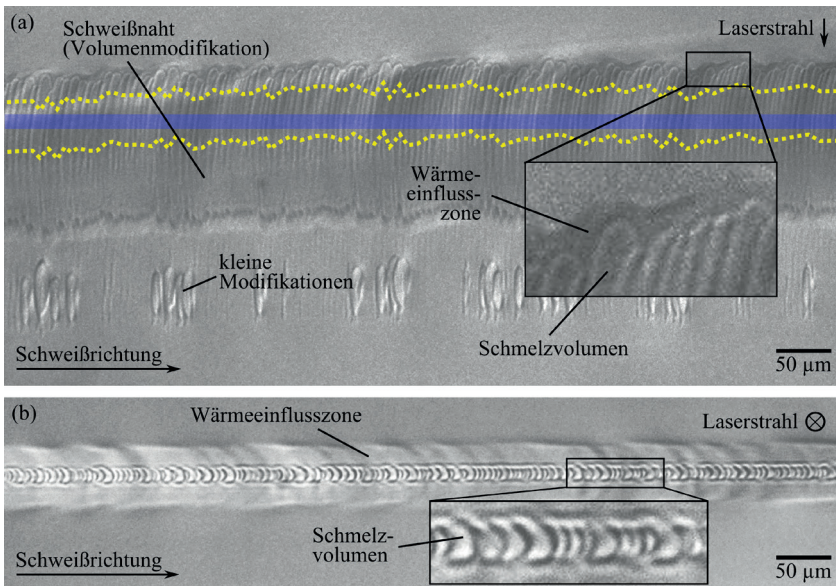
Mit konstanter mittlerer Laserleistung erzeugte Volumenmodifikation in Alkali-Aluminosilikatglas. (a) Seitenansicht und (b) Draufsicht. Die gelben Punkte markieren den lokalen Toleranzbereich für die Position einer Grenzfläche. Der blaue Bereich markiert den resultierenden Toleranzbereich für die gesamte Schweißnaht. [73]
